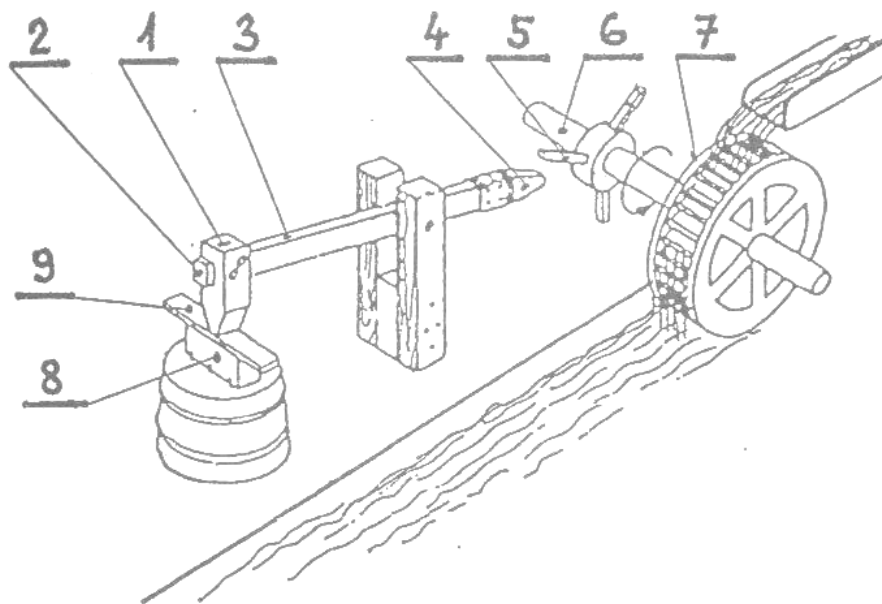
Jednoduchá mechanizovaná kladiva[1]
